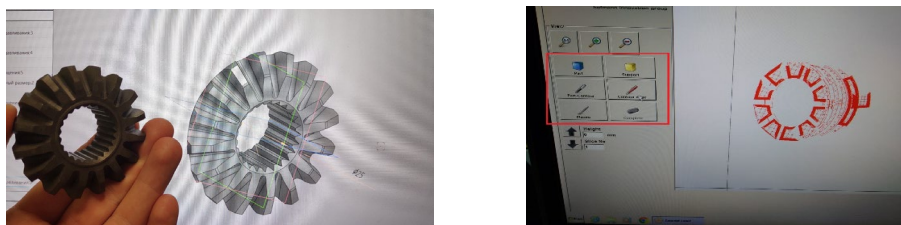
Подготовка принтера к печати: конструирование модели шестерни и подготовка набора поперечных сечений
